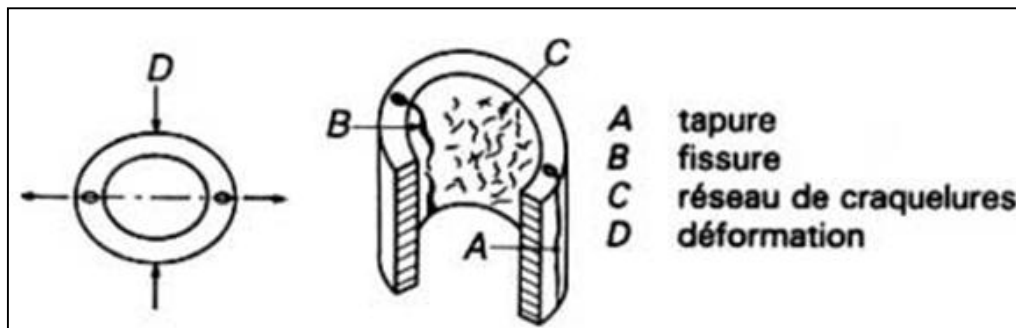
Endommagement des éprouvettes d'essai de choc thermique.
